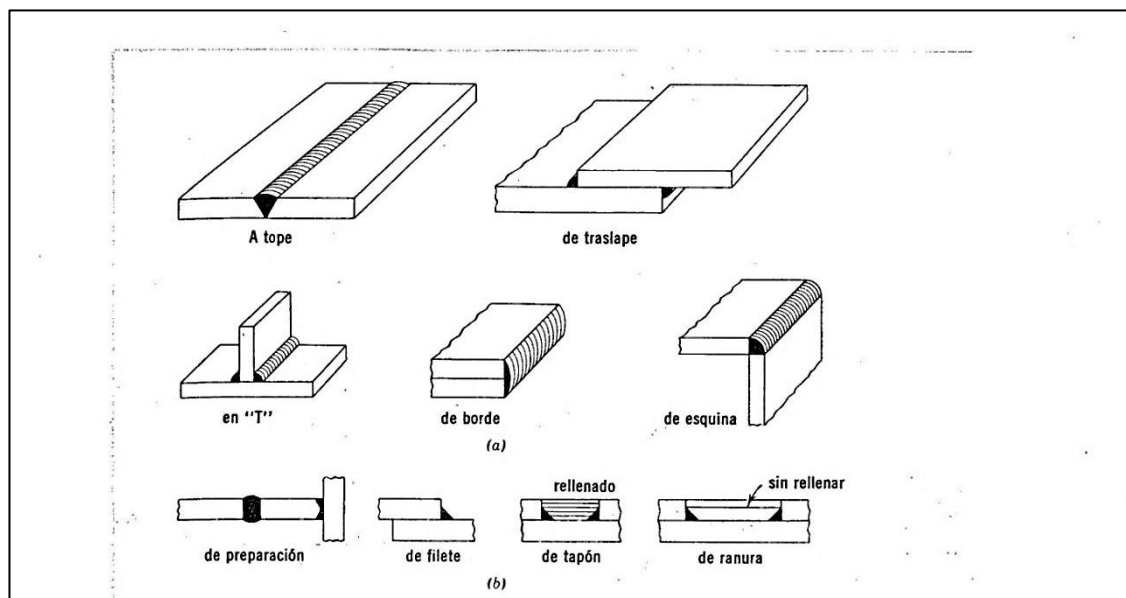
Tipo de conexiones soldadas y soldaduras
